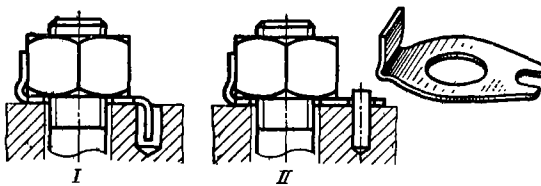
Способы фиксации стопорной шайбы на корпусе
